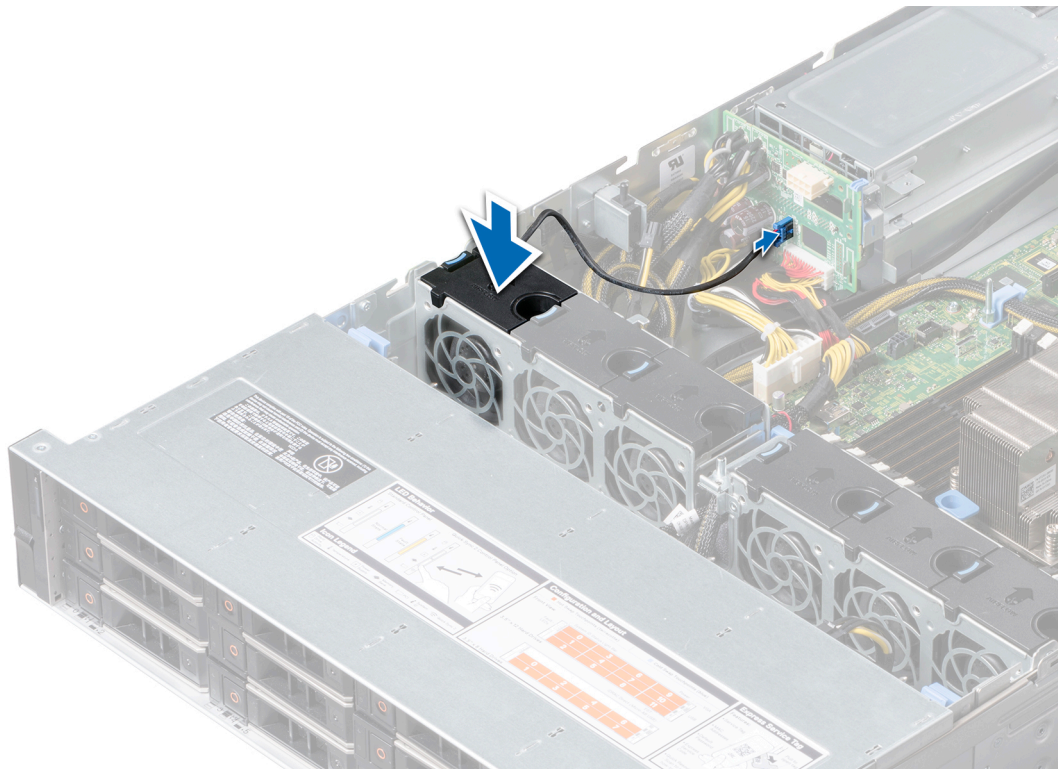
Branchement du câble du ventilateur sur le connecteur PIB
